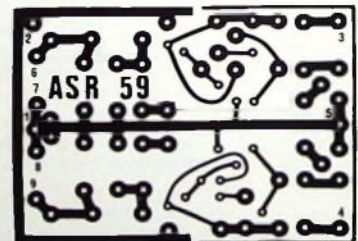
Printplatte des Aussteuerungsmessers für Batteriebetrieb (Maßstab 1:2)
